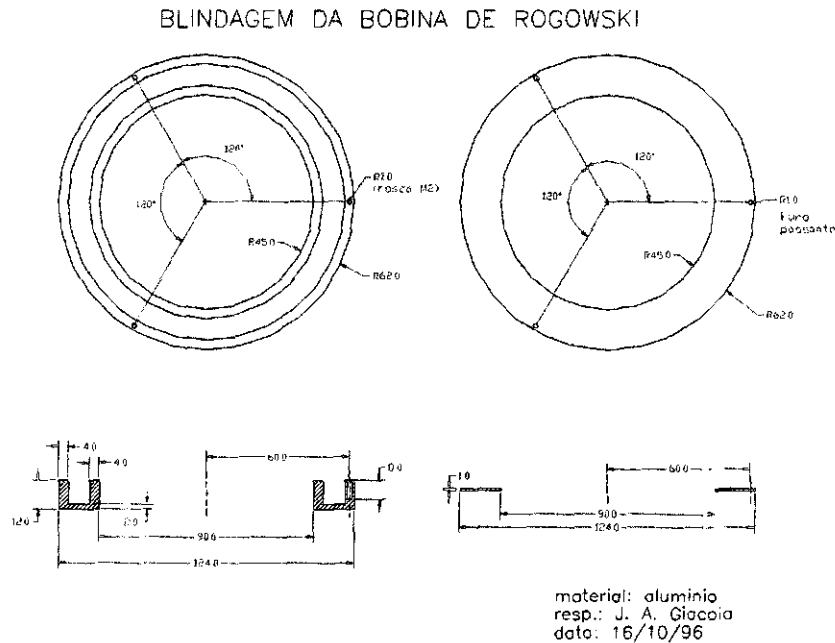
Blindagem de alumínio para a bobina de Rogowski.
